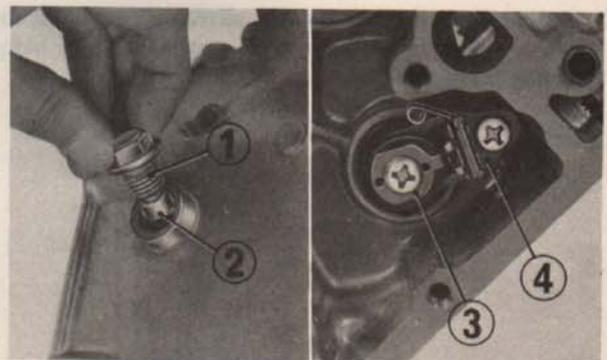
(1) Ecrou de guidage de tambour sélecteur de vitesses
